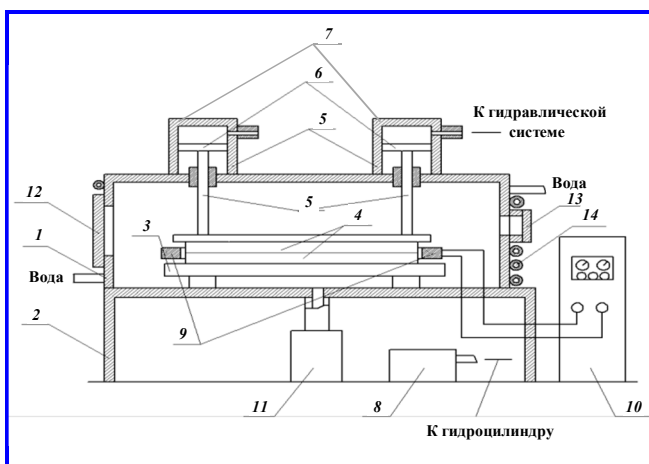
Схема типовой установки для диффузионной сварки: 1 – корпус камеры; 2 – основание; 3 – стол; 4 – свариваемые детали; 5 – шток; 6 – поршень; 7 – цилиндр; 8 – гидравлическая система; 9 – нагреватель; 10 – источник тока; 11 – вакуумная система; 12 – загрузочный люк; 13 – смотровое окно; 14 – система водяного охлаждения
